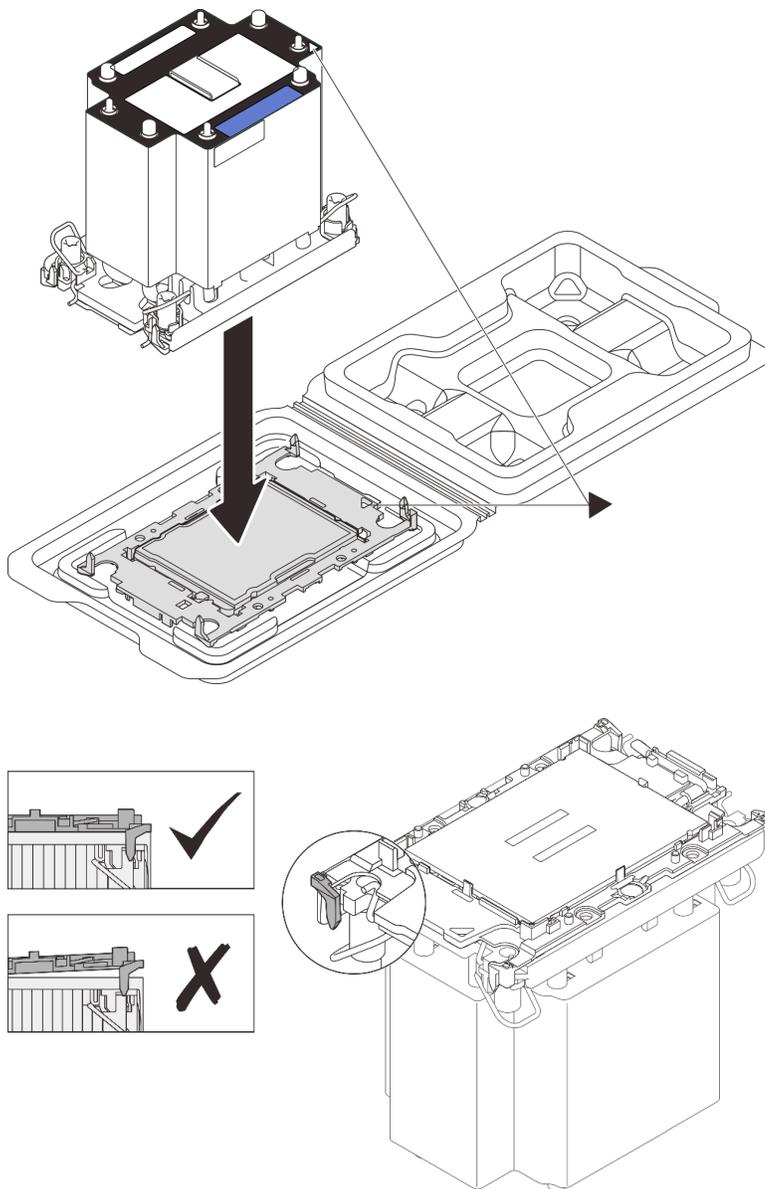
Assemblage du module de processeur-dissipateur thermique avec le processeur dans le plateau d'expédition
